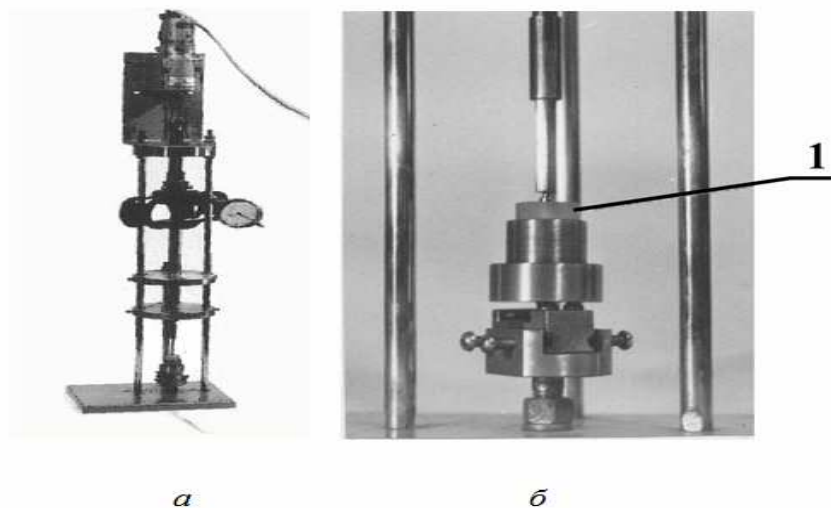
Установка для механічних випробувань на відрив: а – загальний вигляд установки для механічних випробувань зварних вузлів; б – пристрій для установки вузла (макета), що випробується (поз. 1)
